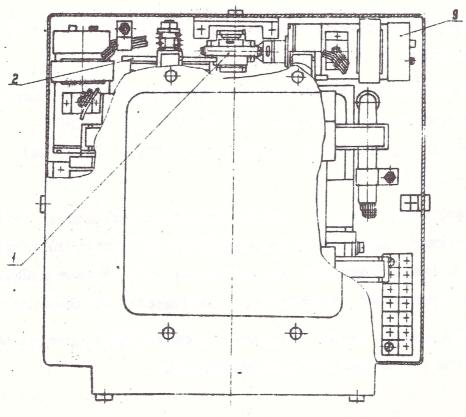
1-Редумтор; 2-Нуфта: 3- Упор; 4-Кечтия, 5-Шторка; 6-Шторка; 7-Шторка; 8-Болт, 9-Электродвига тель
